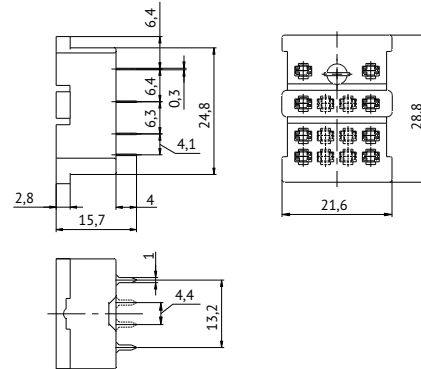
Габаритные, установочные, присоединительные размеры розеток OptiRel G RR94-1X
